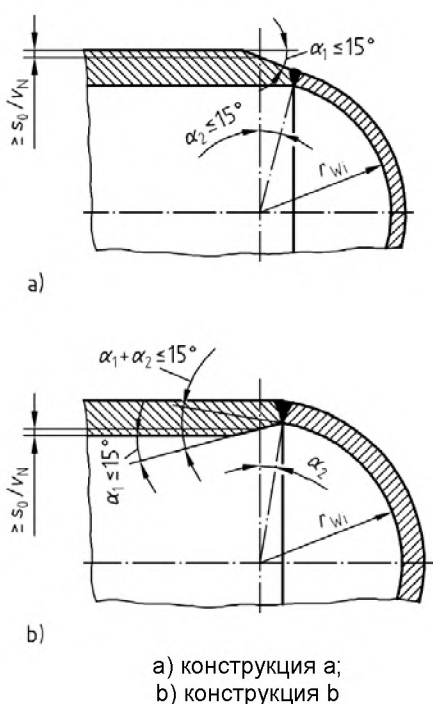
Сварное соединение полусферического днища и цилиндрической части с большей толщиной стенки
